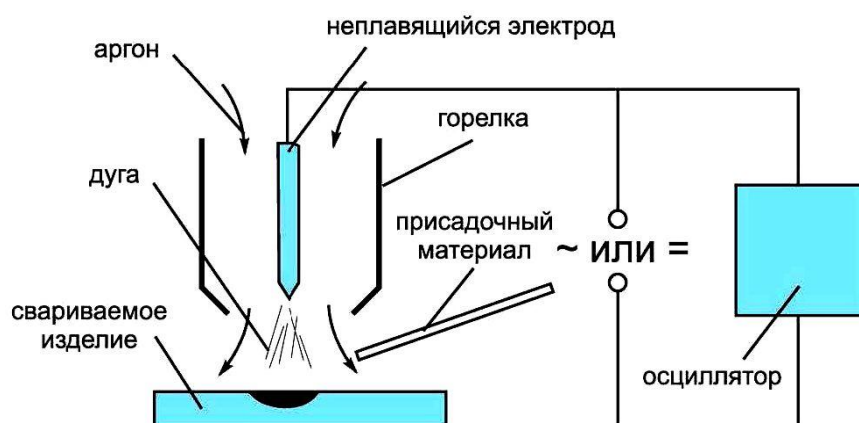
Сварка неплавящимся электродом в защитном газе
